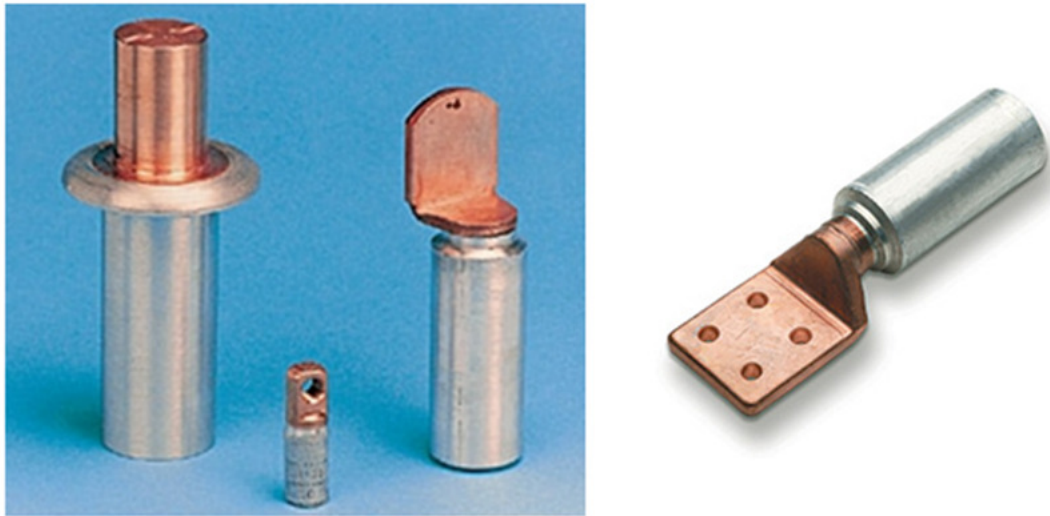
Solda a fricção entre Alumínio e Cobre<sup>(22)</sup>.
